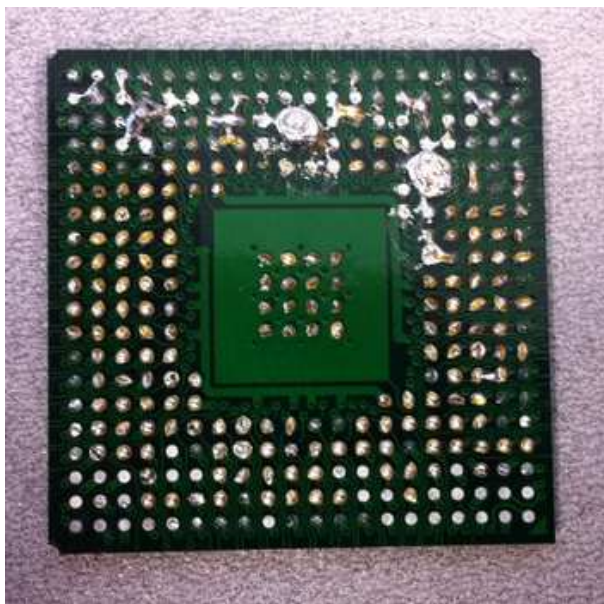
Základní deska počítače po demontáži pouzdra BGA
